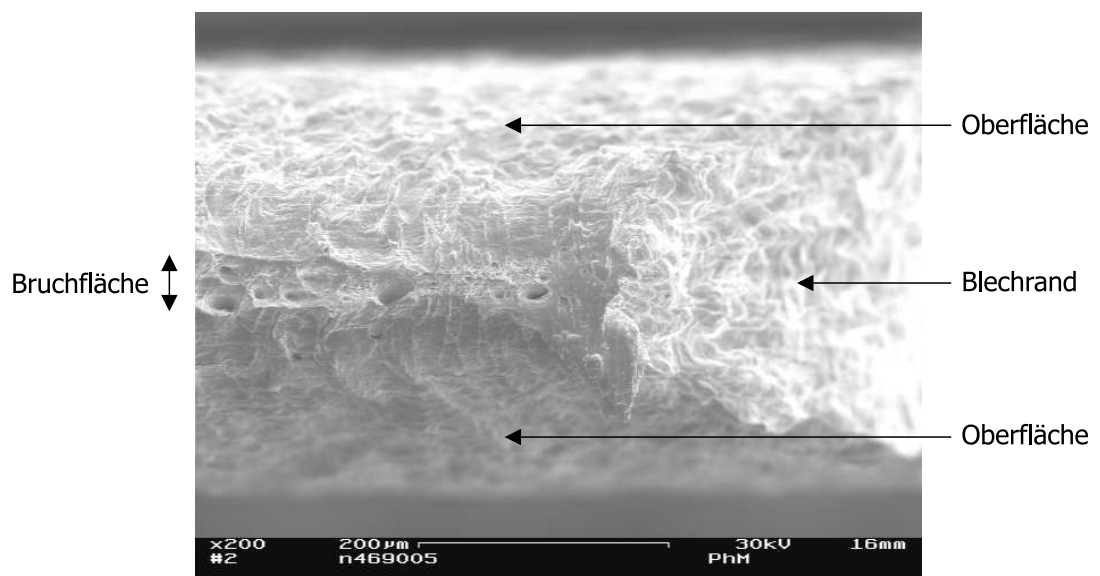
Aufsicht (entlang der Zugrichtung) auf die Bruchfläche des dicken Randes der keilförmig geschliffenen Zugprobe des Blechs 3.
